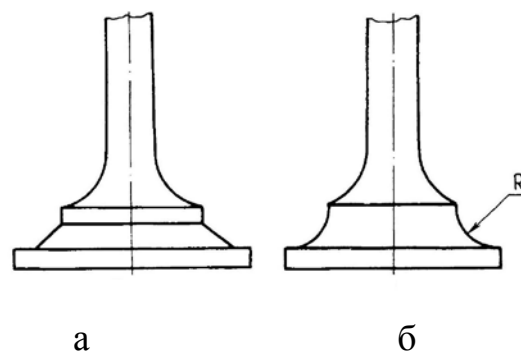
Трапецевидна (а) і радіусна (б) розробка заготовок клапанів під наплавку [1]
